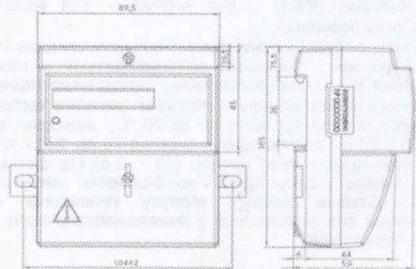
Загальний вигляд лічильника ЦЭ6807Б-У в корпусі Р5.1
